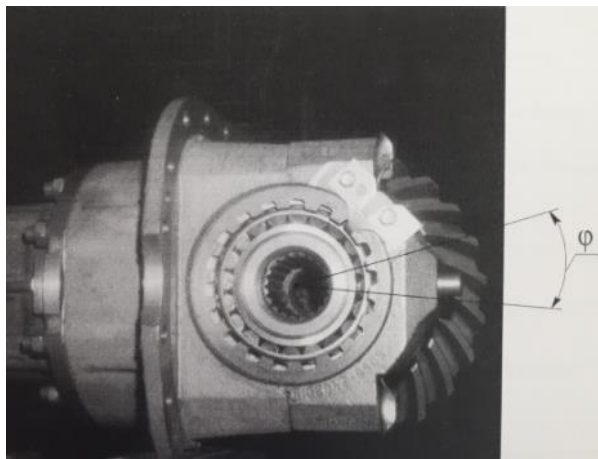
Гнездо подшипника дифференциала в сборе с резьбовым корончатым регулировочным кольцом и стопором
